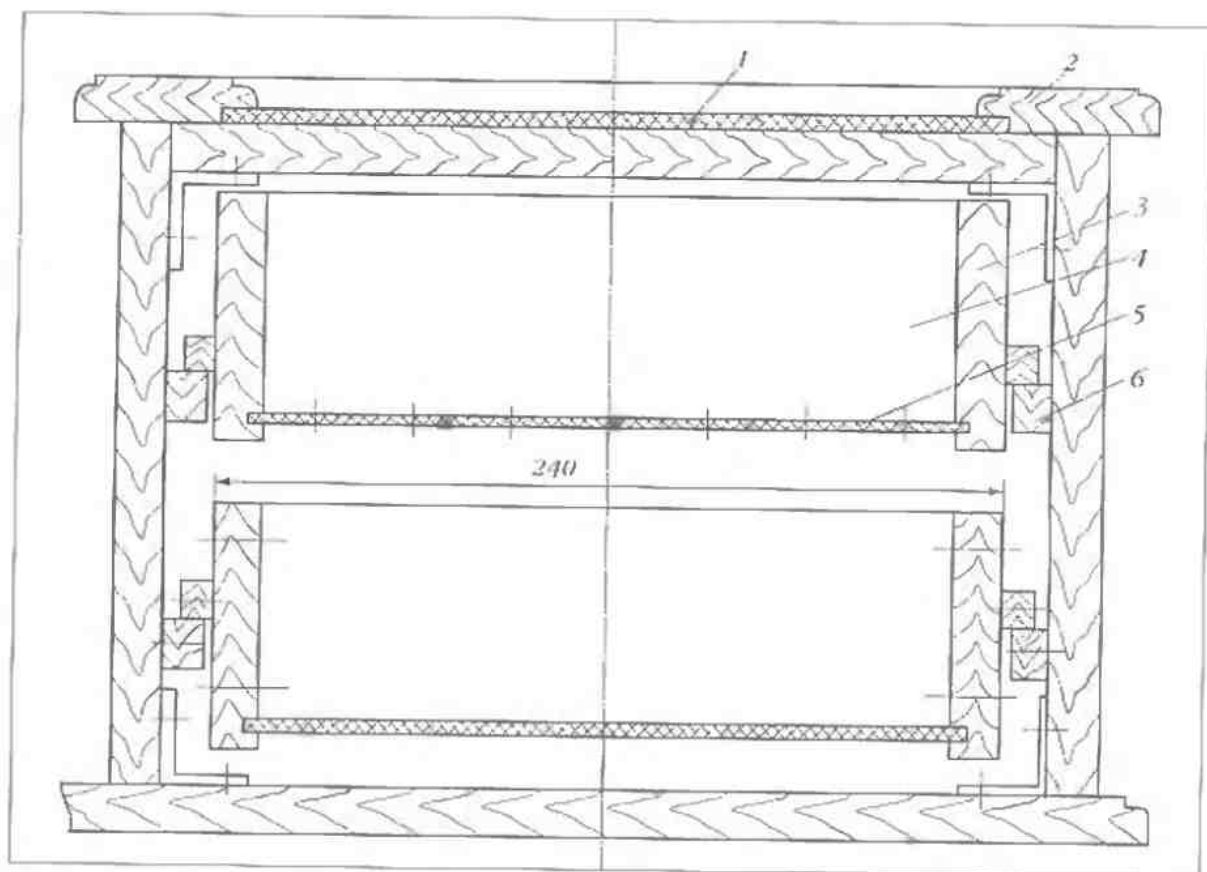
Тумбочка диванчика в разрезе (масштаб 1:2): 1 – вкладыш (лист ДВП, обитый тканью); 2 – верхняя крышка тумбочки; 3 – боковина ящика; 4 – задняя стенка ящика; 5 – дно ящика; 6 – напращивающая рейка
